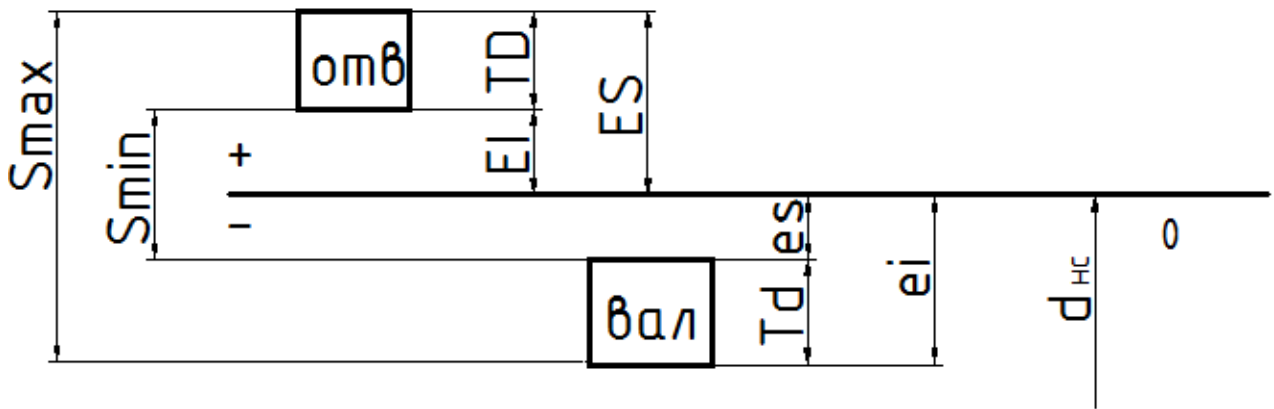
Расположение полей допусков отверстия и вала для посадки с зазором
